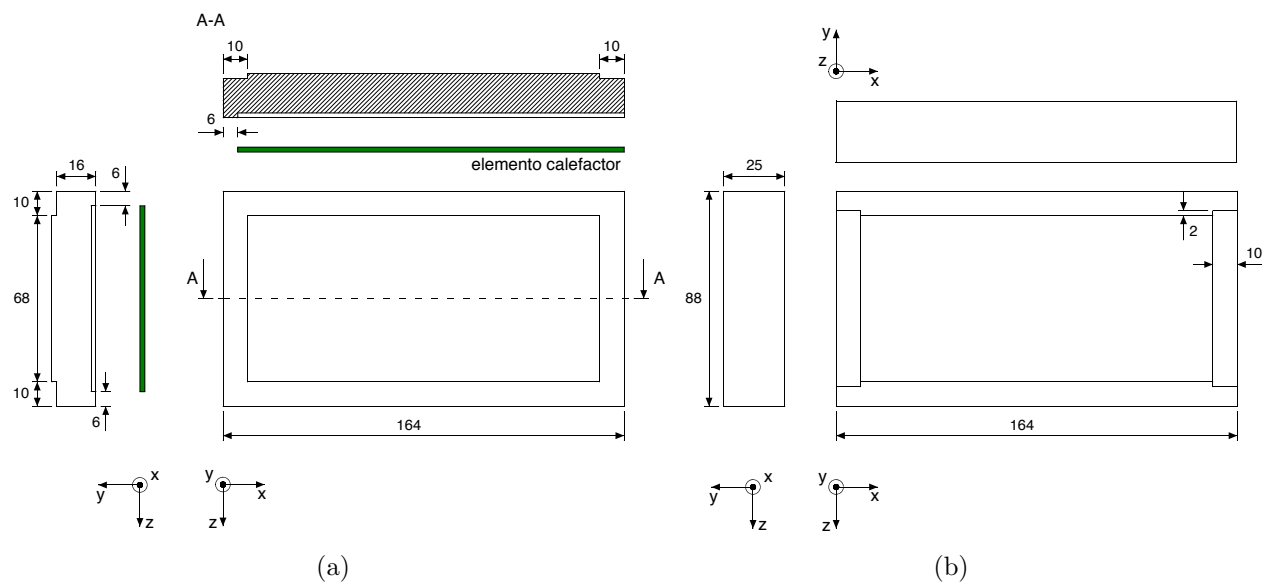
Dimensiones principales de (a) placa caliente y elemento calefactor y (b) paredes laterales.
